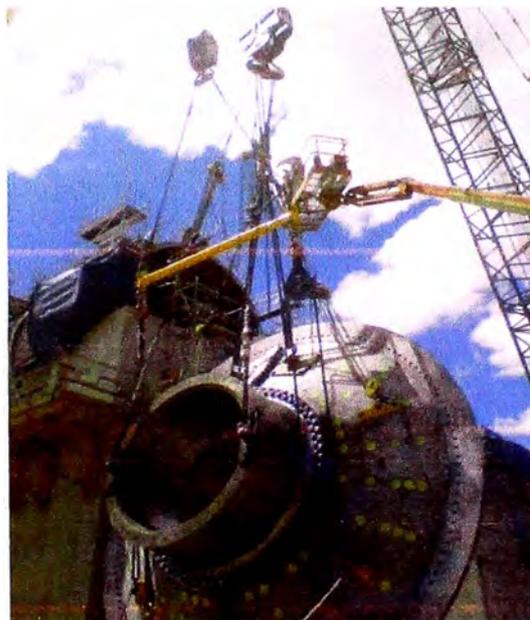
Tandem de tapa-trunnion, (Proyecto Antapaccay).
